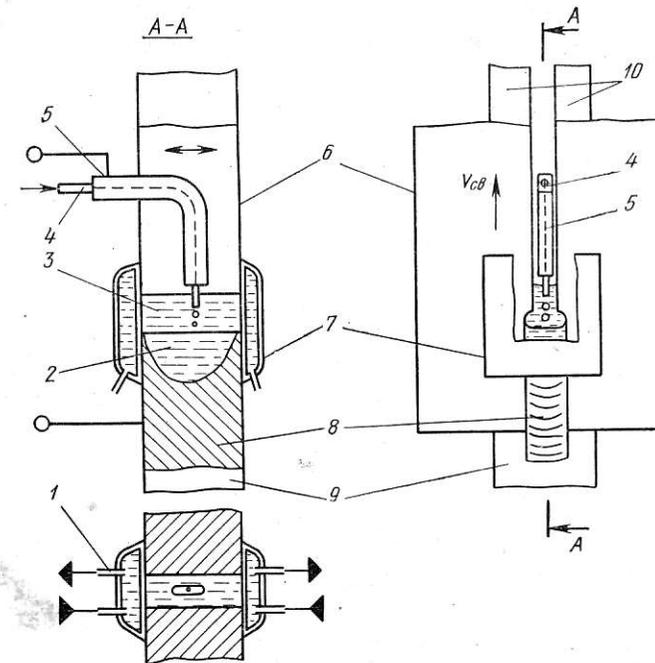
Схема процесса электрошлаковой сварки
